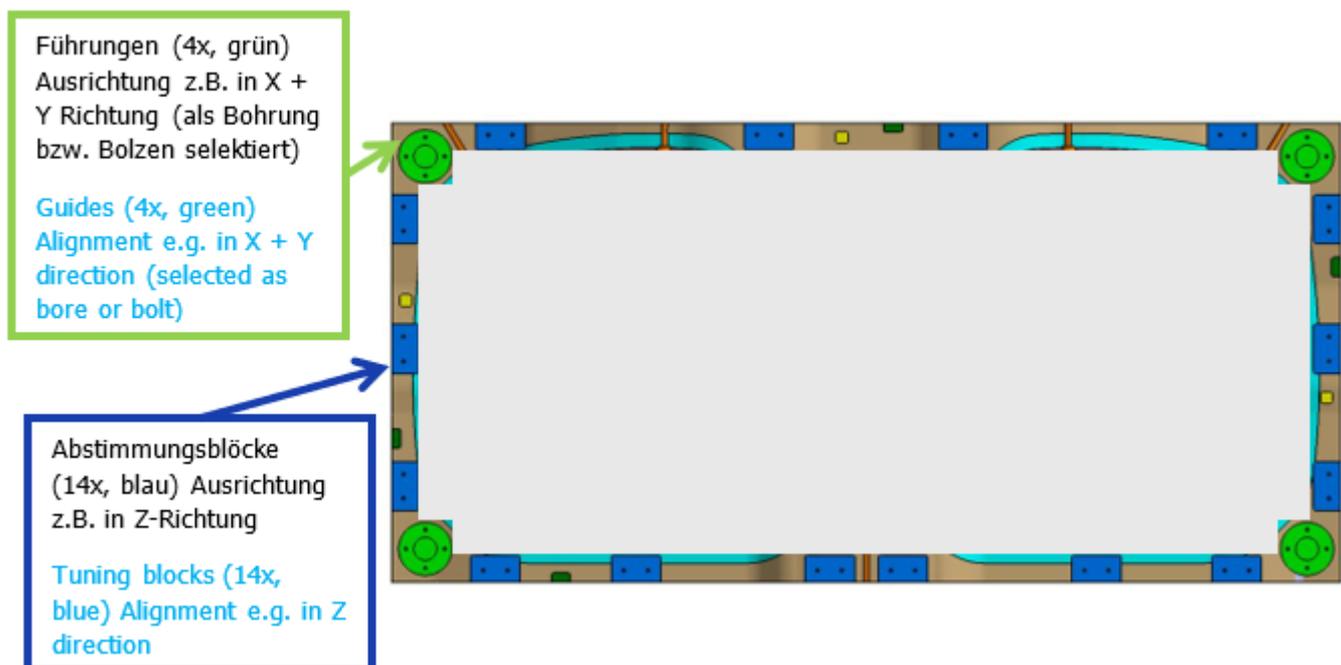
Ausrichtung für Werkzeuge, Formen und Vorrichtungen
